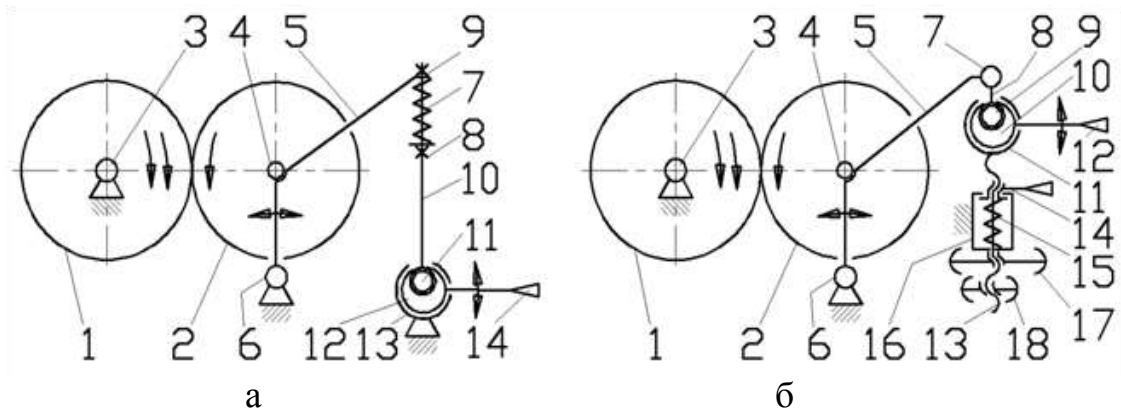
Схеми установчих механізмів вальцьових верстатів.
